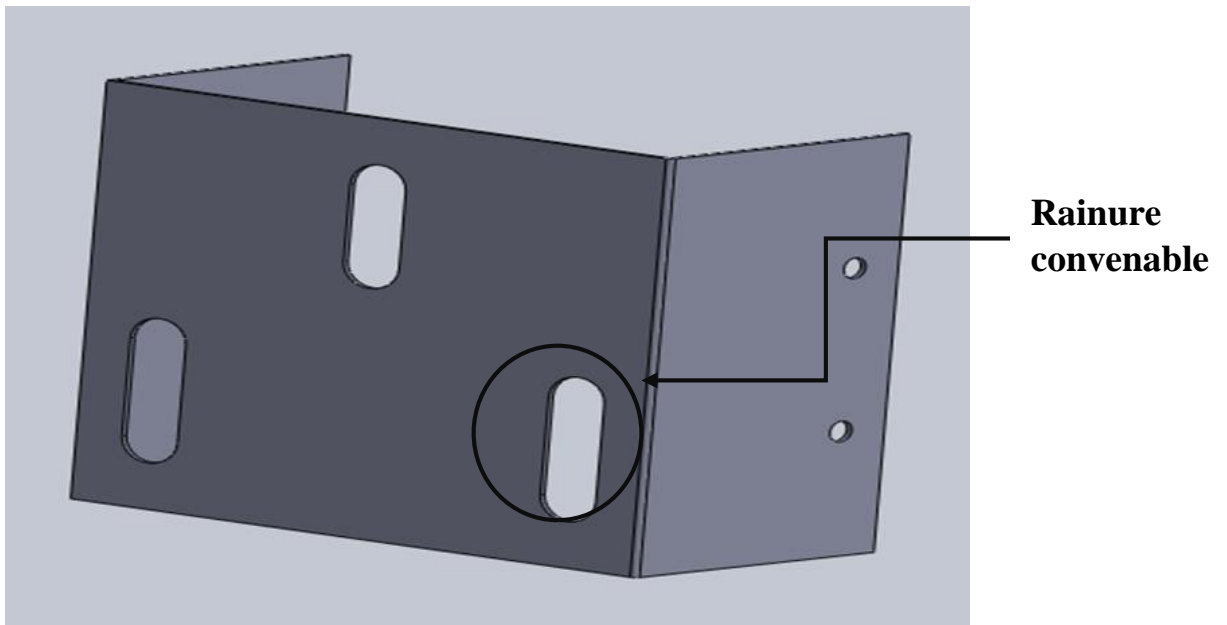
le nouveaux couvercle sur SOLIDWORKS
